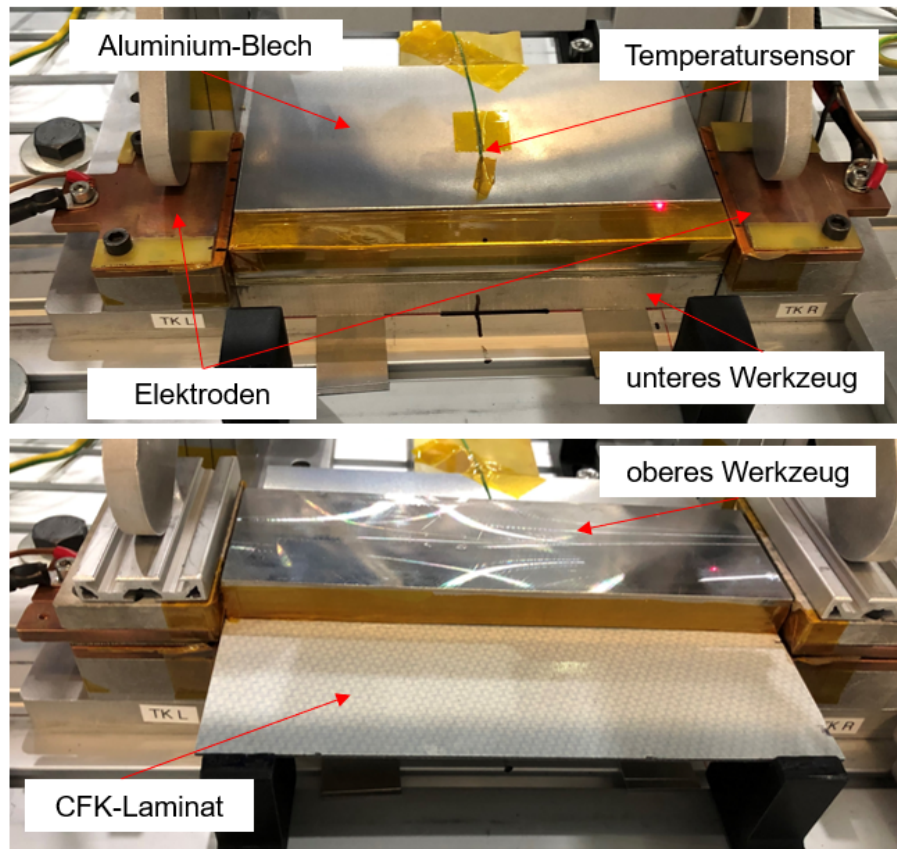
Aufbau der Schweißanlage zum elektrischen Widerstandsschweißen
